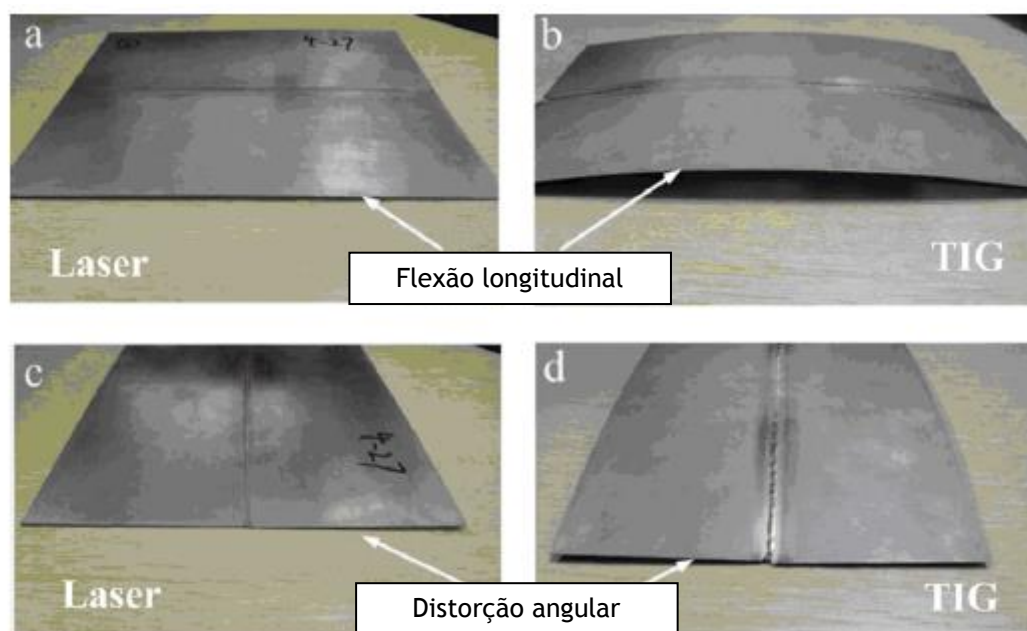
Distorções após soldadura: a) flexão longitudinal por laser; b) flexão longitudinal por TIG; c) distorção angular por laser; d) distorção angular por TIG
